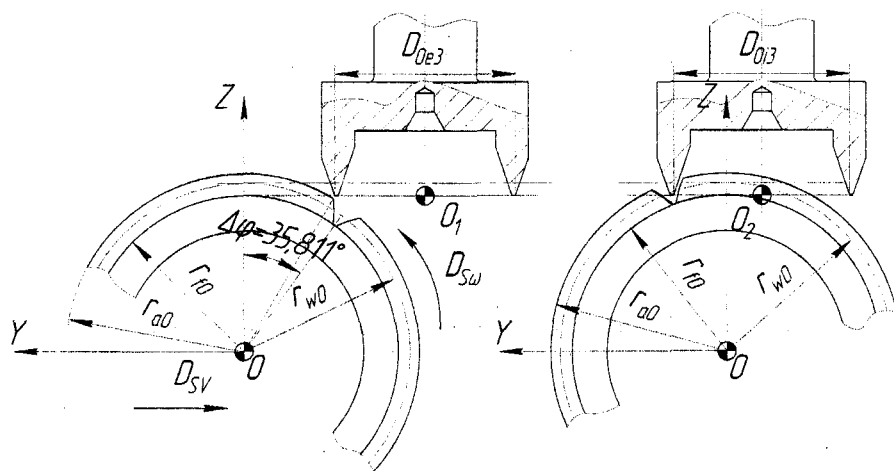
Движение обката при чистовой обработке вогнутой стороны зуба инструмента односторонней зуборезной резцовой головкой
